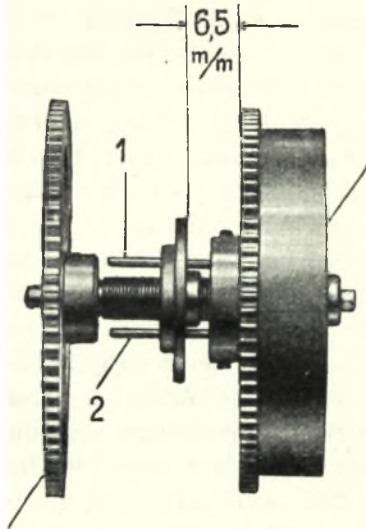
Kontaktsteuerung der Electora-Uhr durch eine Wandermutter
